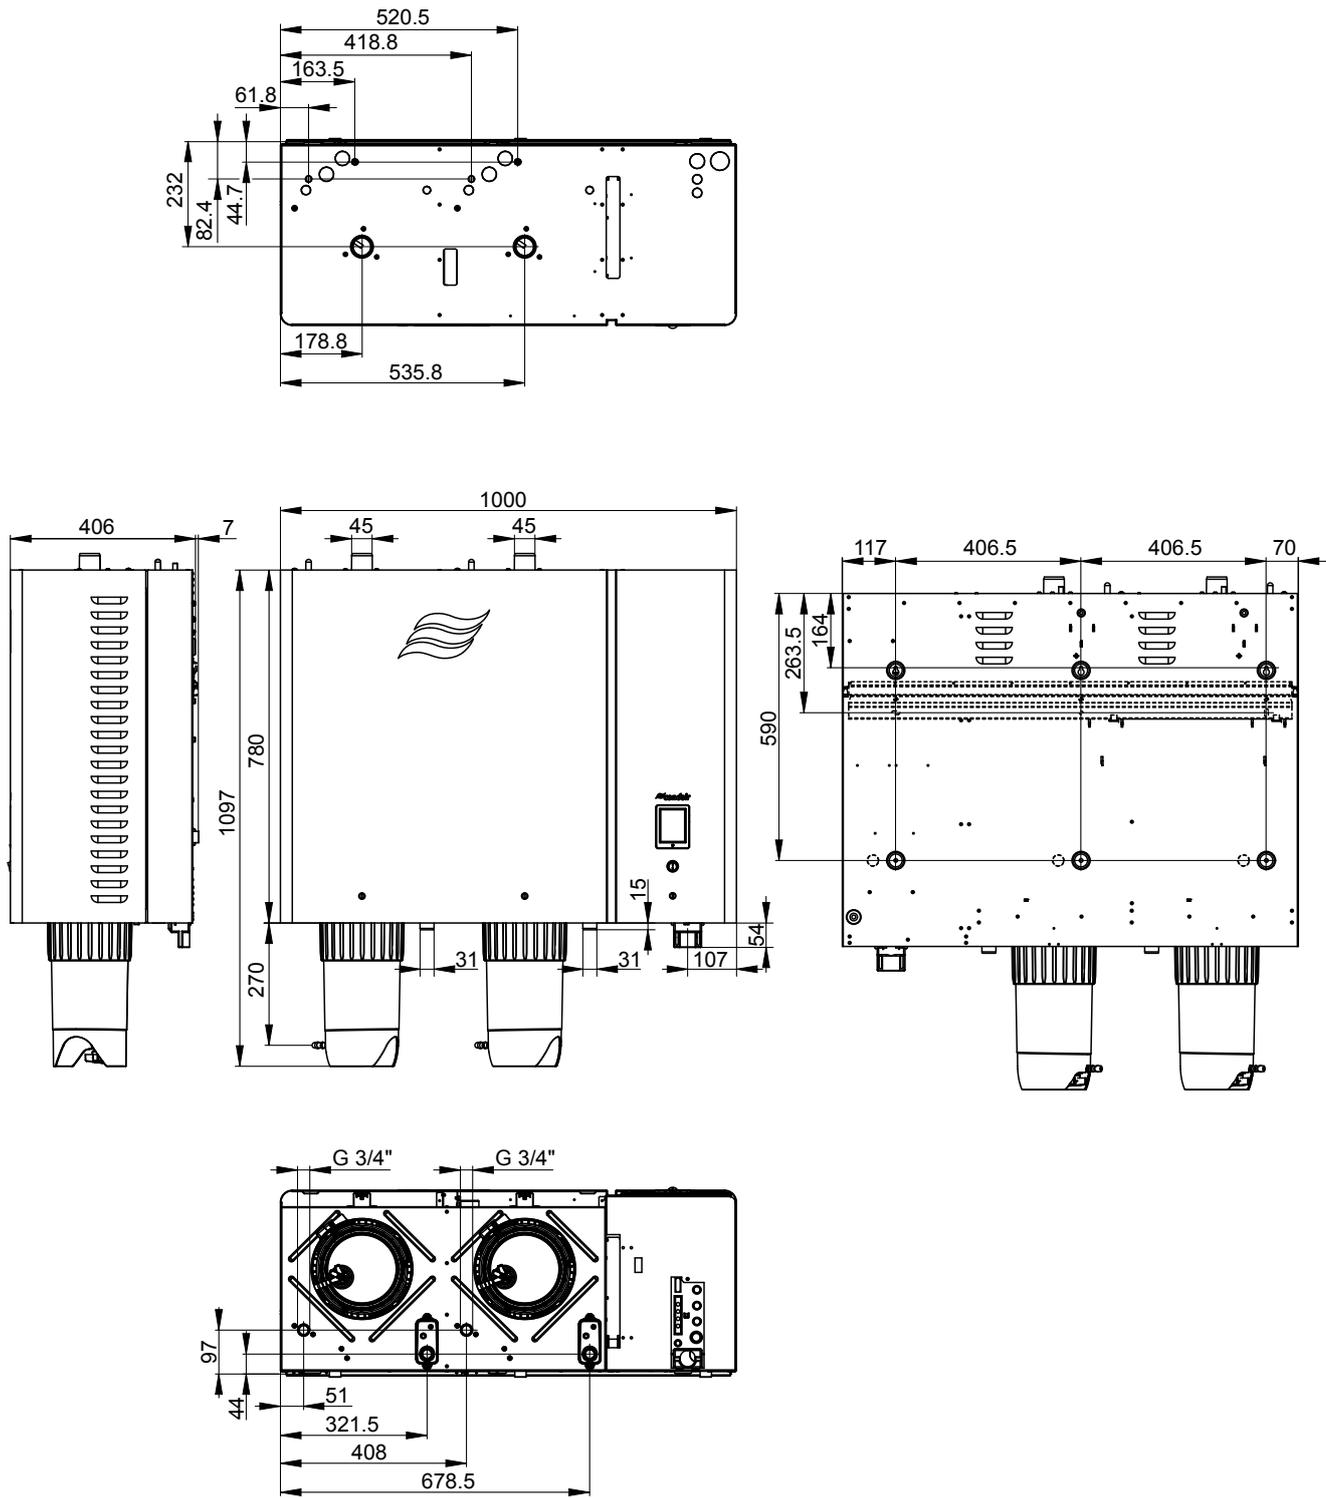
Figura de dimensiones del equipo "L" (dimensiones en mm)
